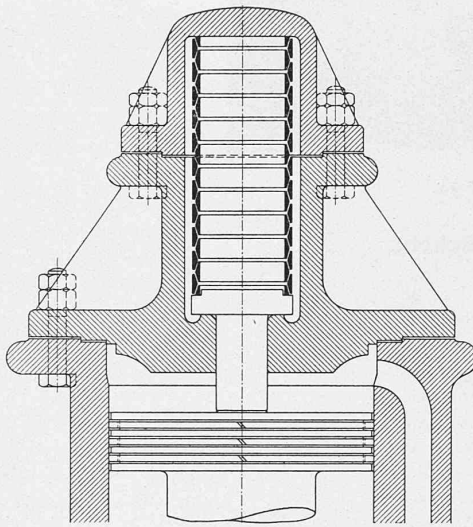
Ringfeder-Kolbenfang für Dampfhämmer.
